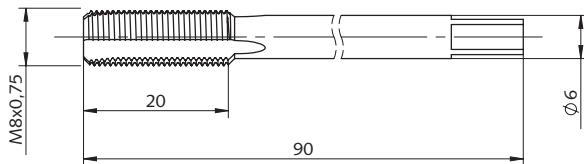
Gewindebohrer M8x0,75 Typ 1361
